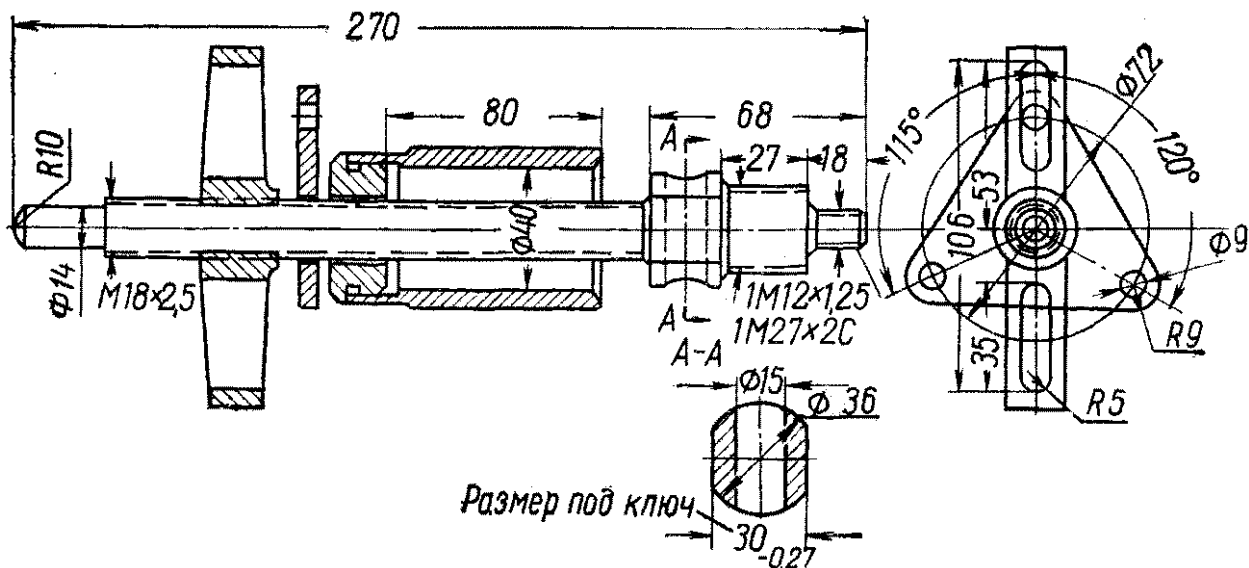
Съемник ступицы шкива и шестерни коленчатого вала, шестерни распределительного вала и ступицы шкива водяного насоса
